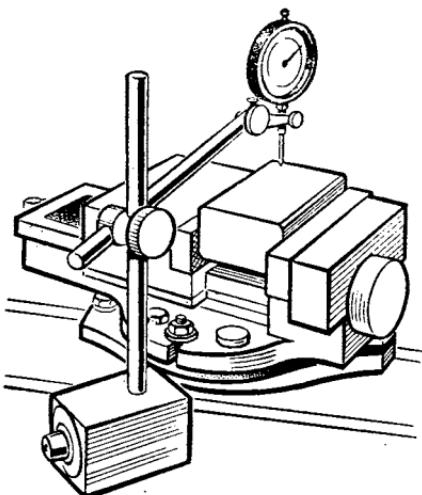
Выверка заготовки при ее установке в тисках перед фрезерованием.
